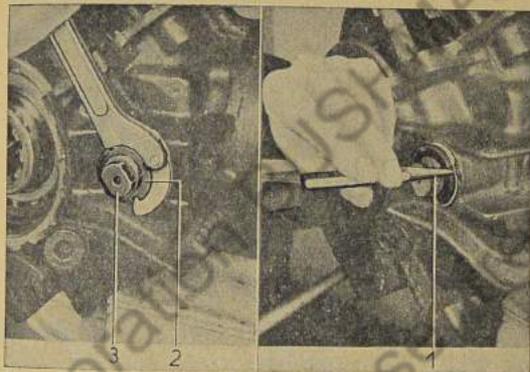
Einstellschraube für Tellerradabstützung zurückdrehen
